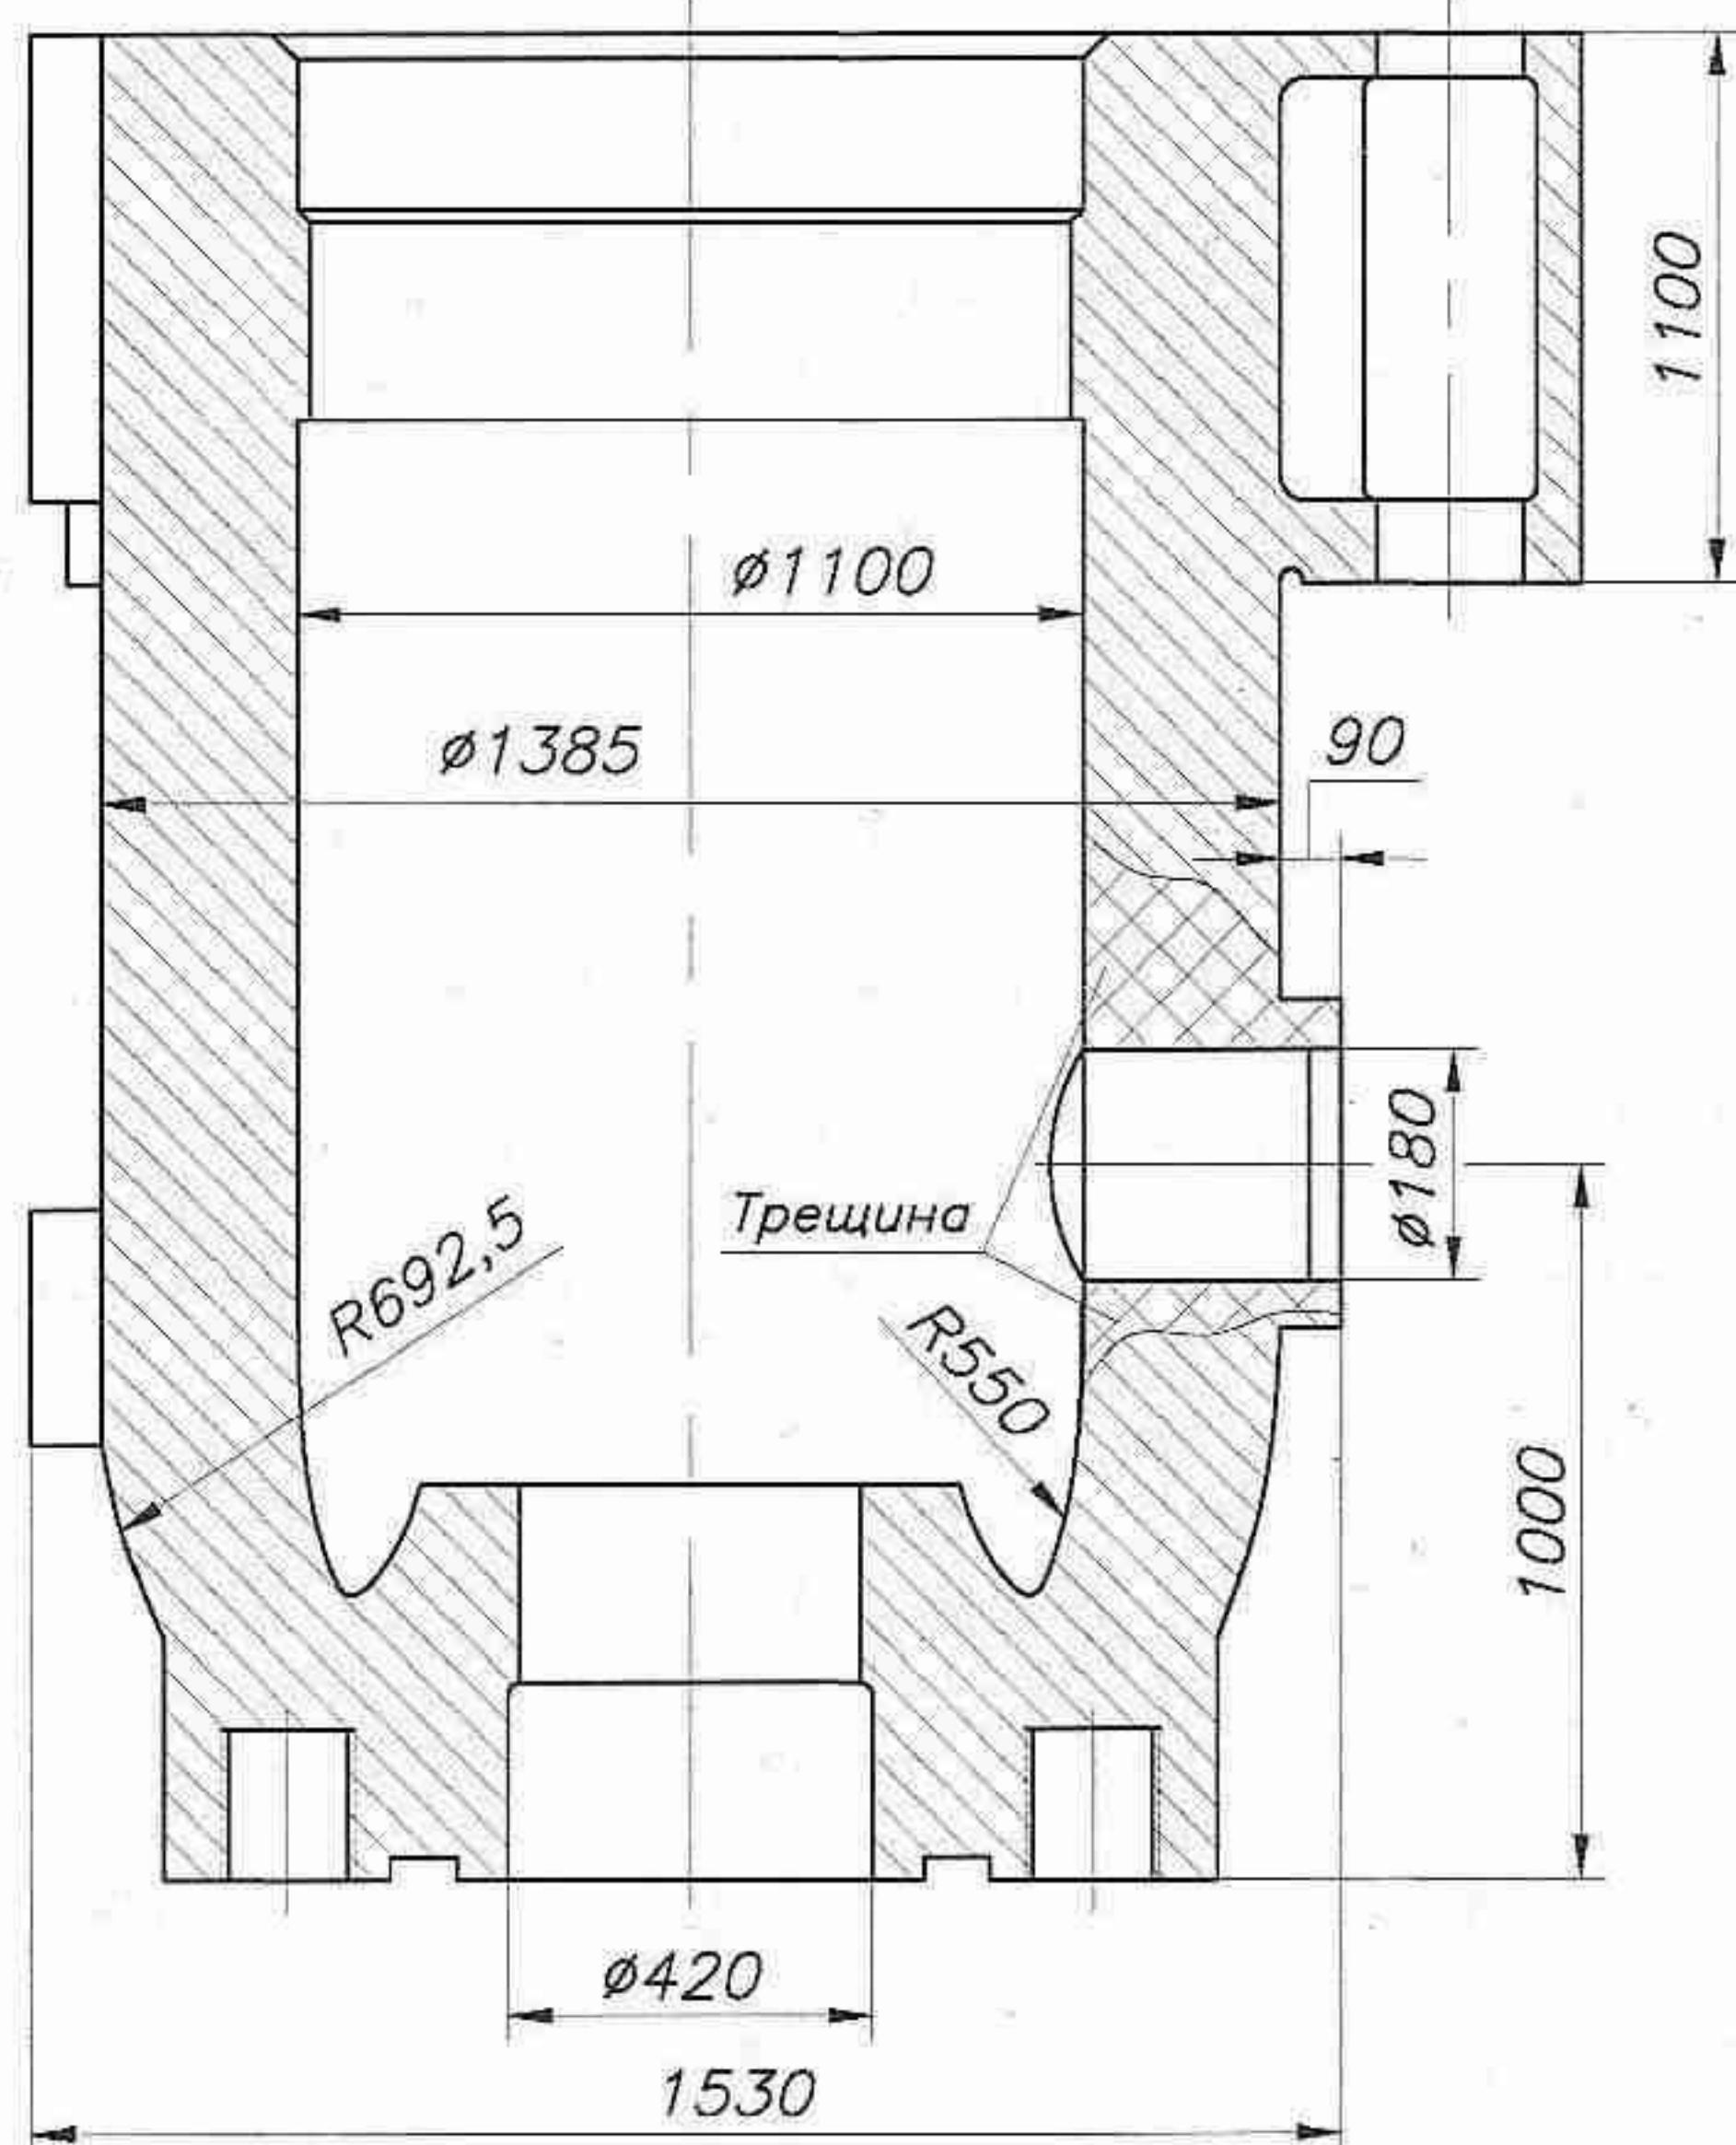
Цилиндр пресса силой 18 МН, разрушенный по отверстию для подвода рабочей жидкости
